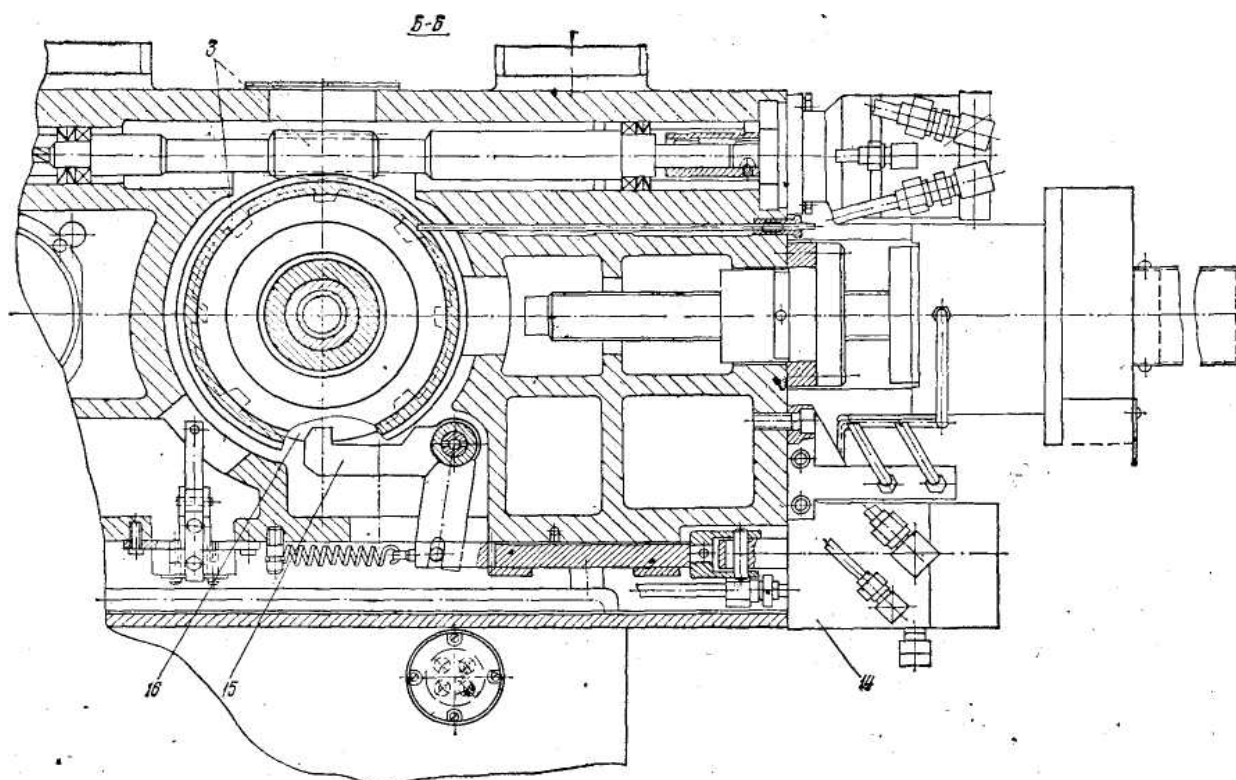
Конструкция револьверного суппорта верстата 1В340Ф30
